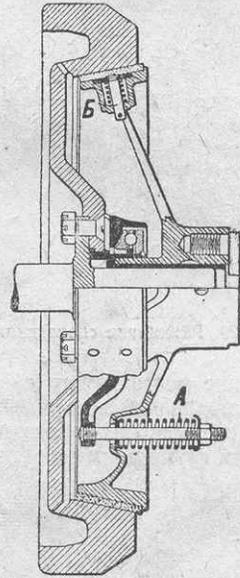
Конусное сцепление с установленными под кожей пружинками.
